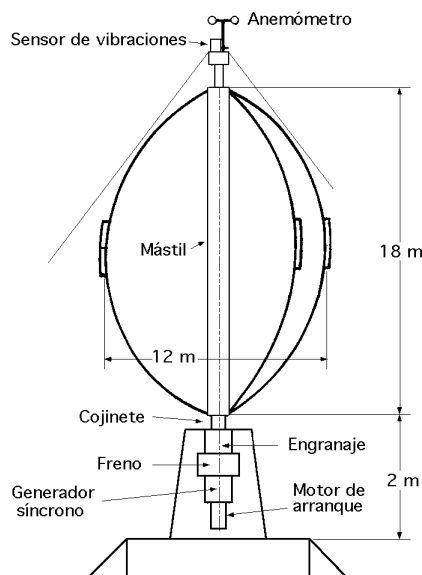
Dimensiones del rotor Darrieux de 25 kW
